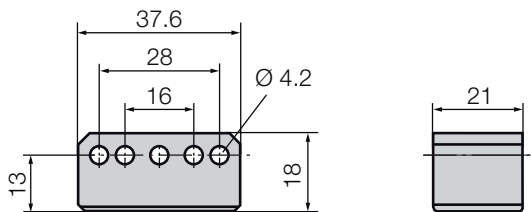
位置指示器BTL6-A-3801-2安装尺寸
